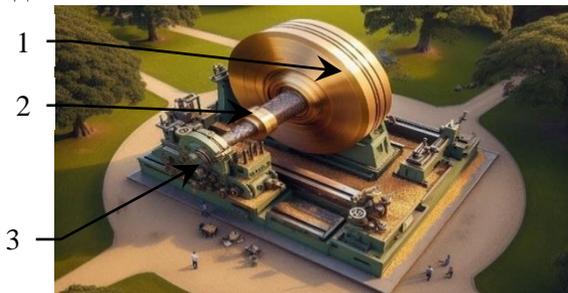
ИИ-интерпретация концепции горизонтально-токарного станка: 1 – обрабатываемая деталь типа диска; 2 – оправка; 3 – шпиндельная бабка
